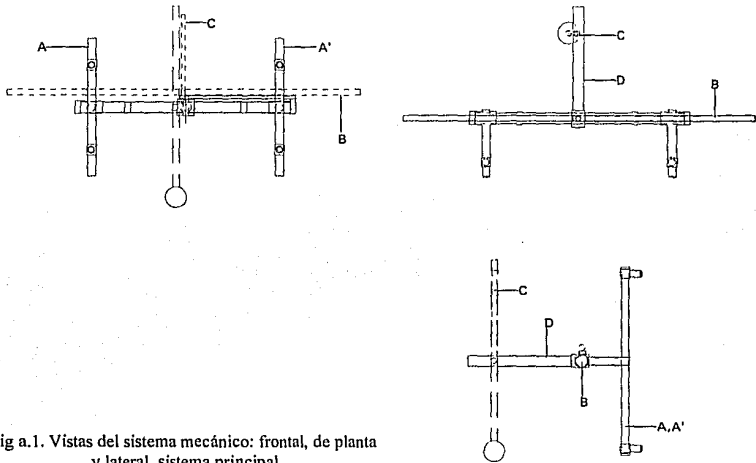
Vistas del sistema mecánico: frontal, de planta y lateral, sistema principal
